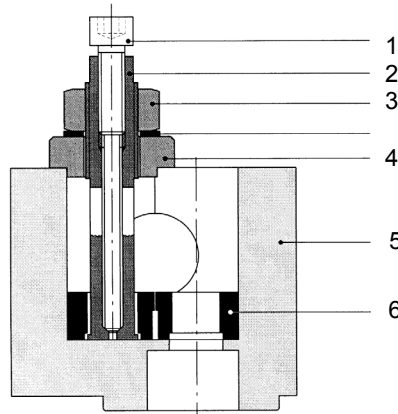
Шестеренчатые насосы типоразмера 22...45, демонтаж подшипника скольжения со стороны привода при помощи устройства для извлечения подшипников
